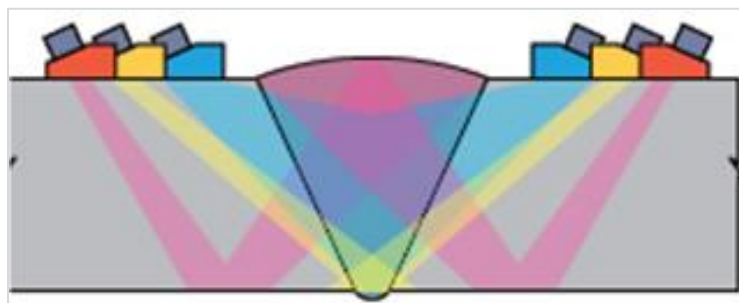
Inspección de una soldadura mediante técnica conjunta UT pulso-eco con TOFD.
